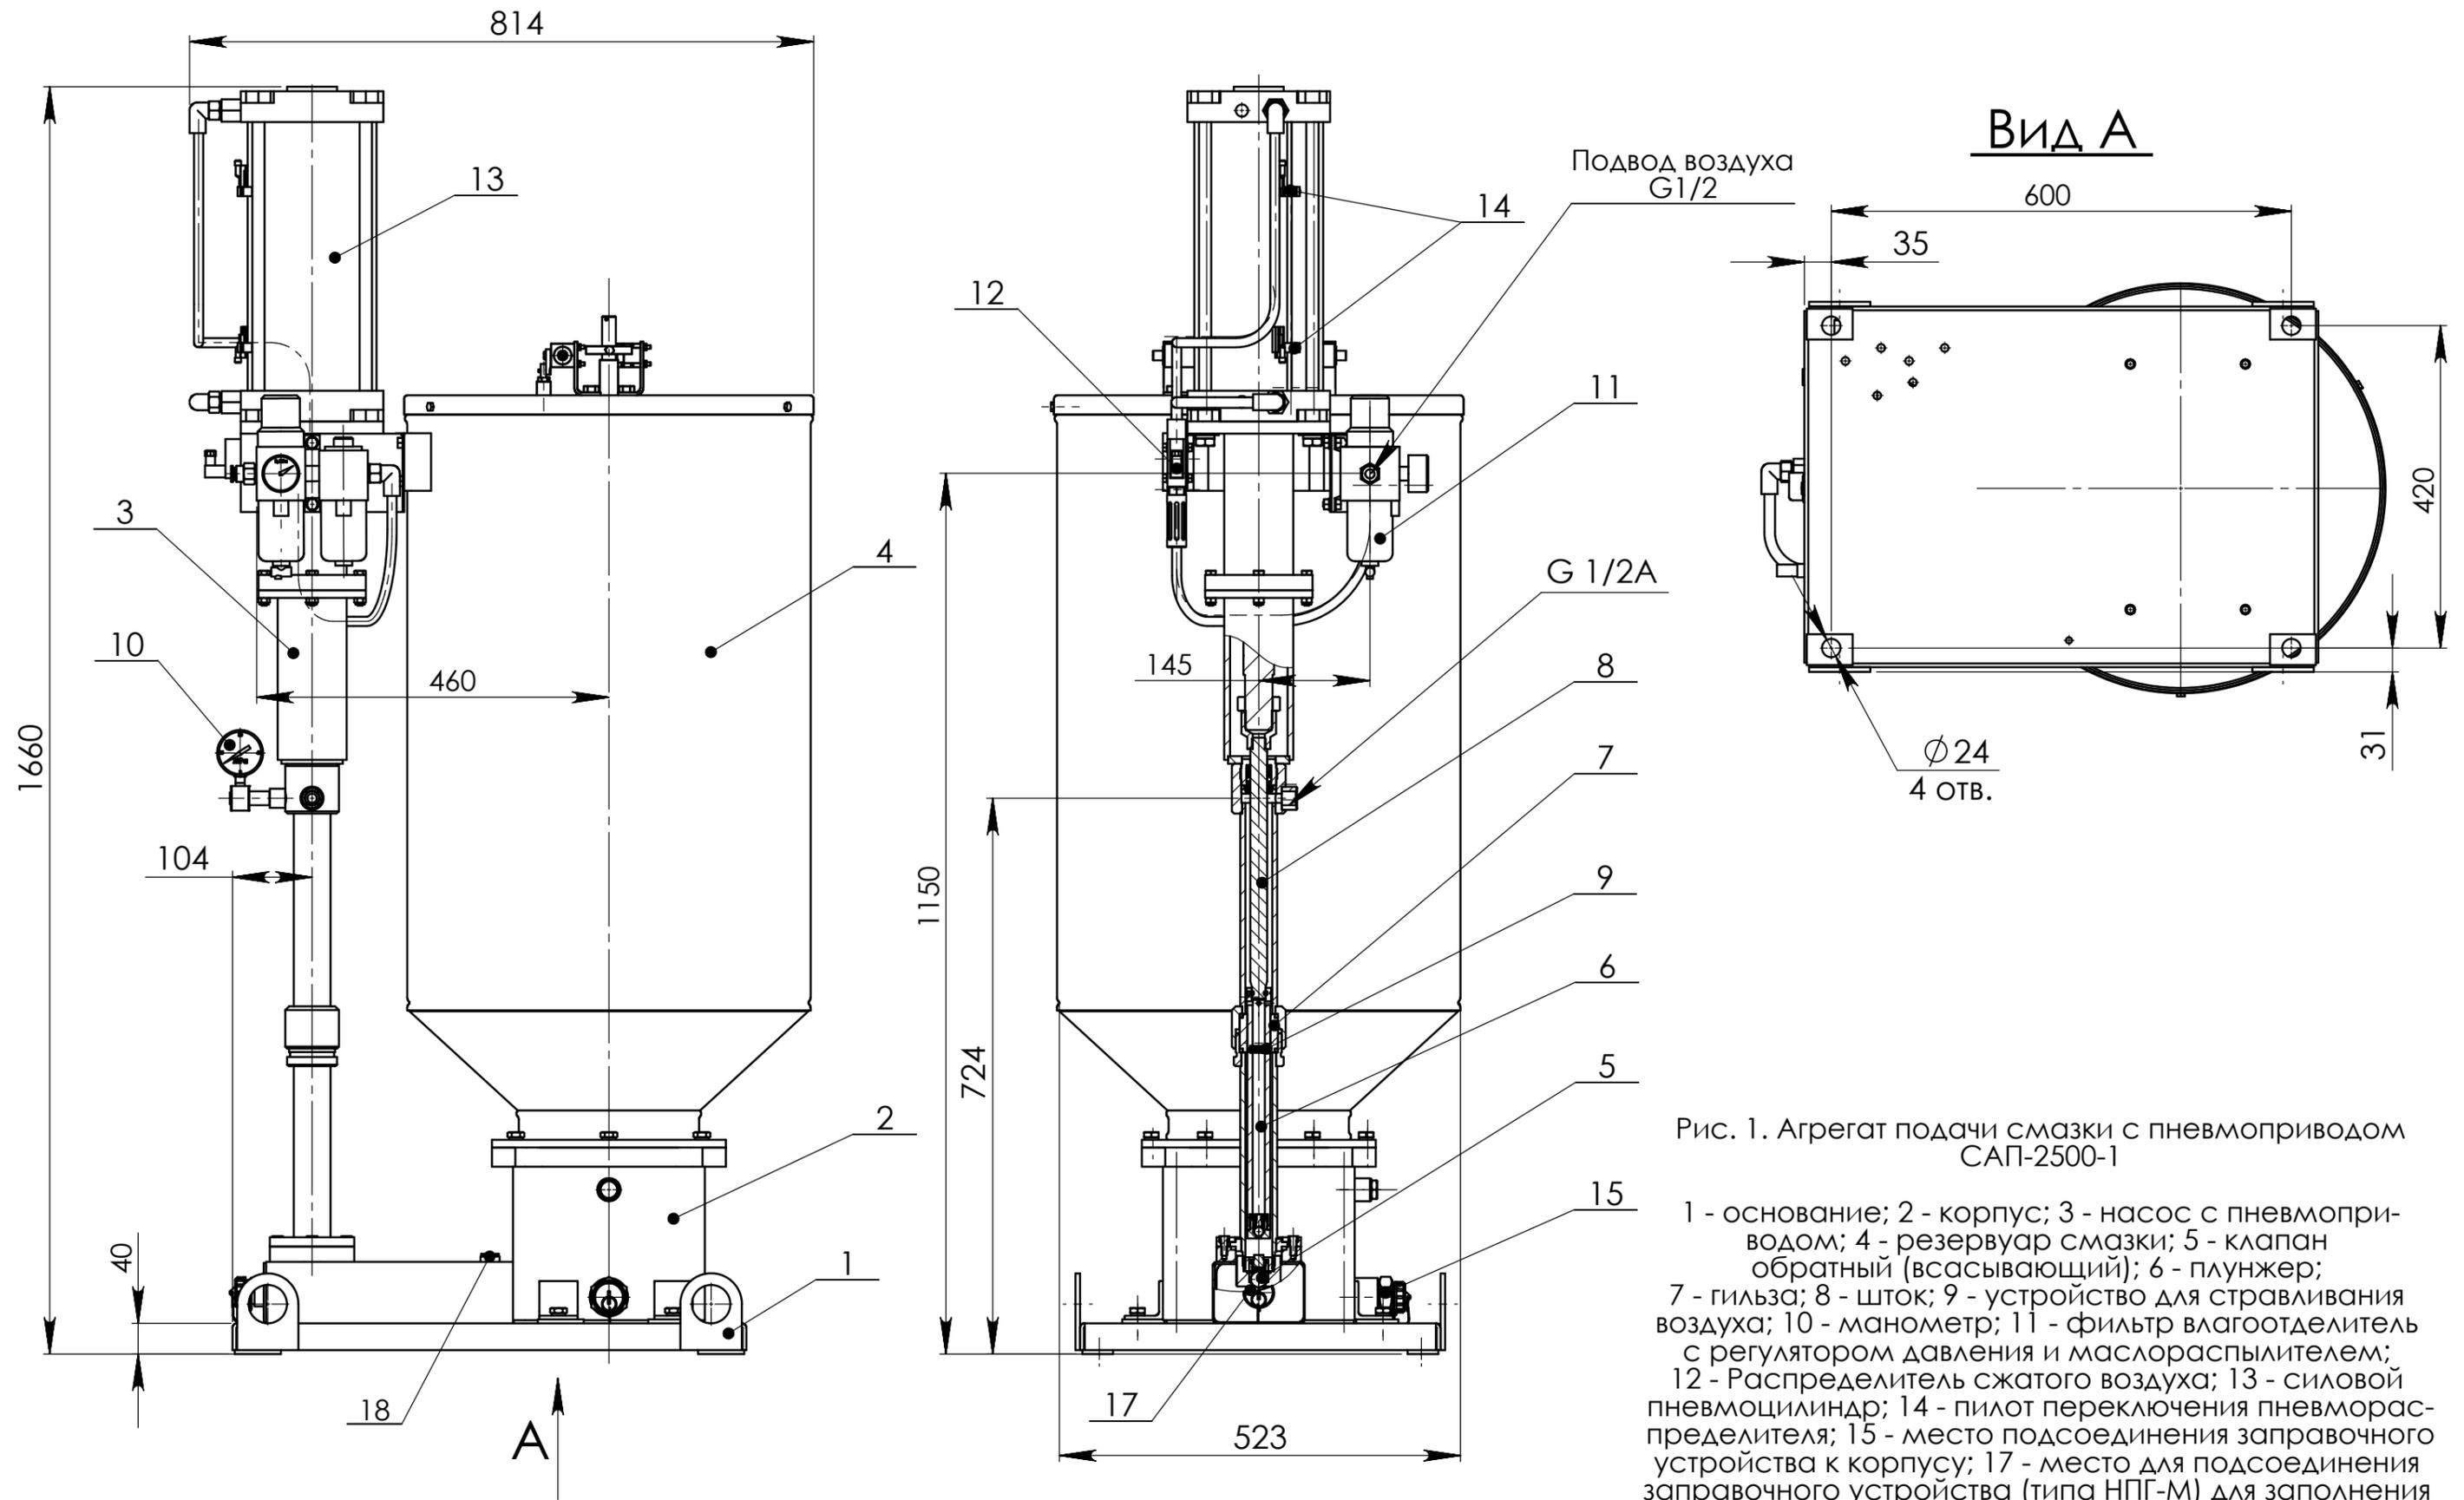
Агрегат подачи смазки с пневмоприводом САП-2500-1
